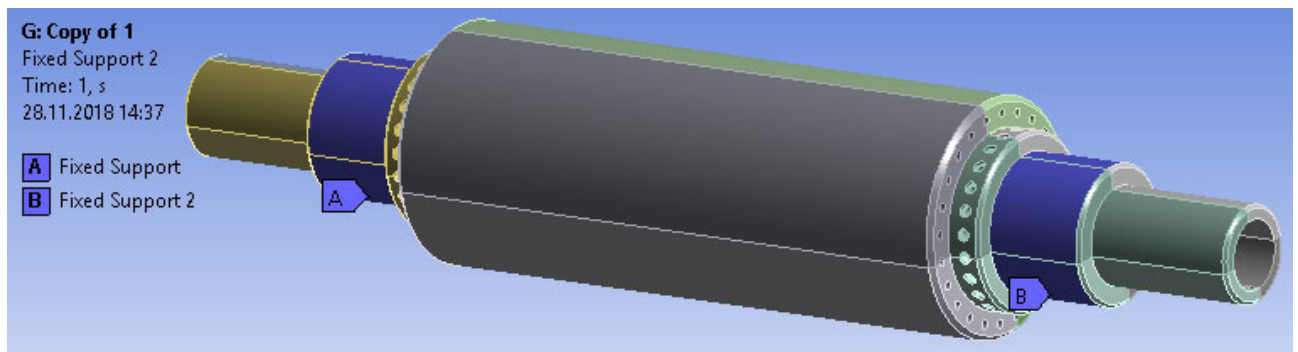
закріплення конструкції модернізованого збірного валка
